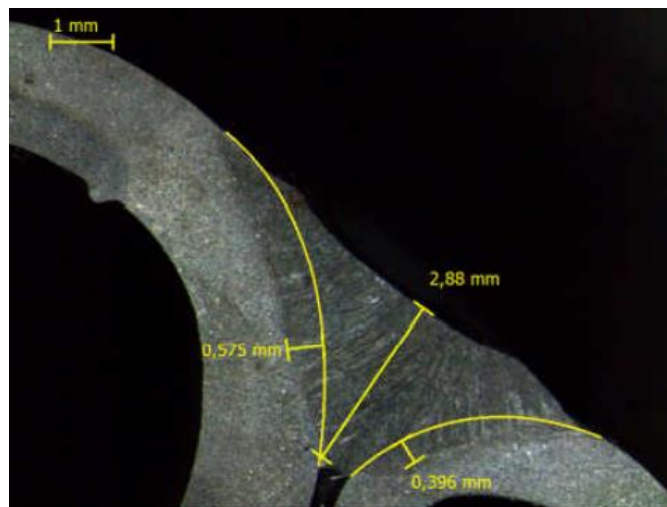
Macrografia do ponto 5.1 com soldadura linear mais larga (Penetração no silêncio de 0,396mm e no gancho de 0,575mm)
